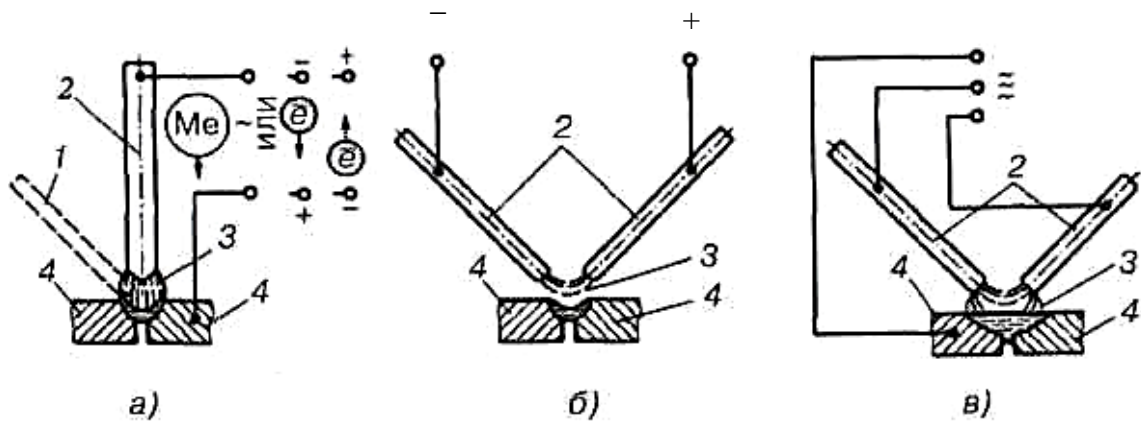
Схемы дуговой сварки: а – дуга прямого действия;
